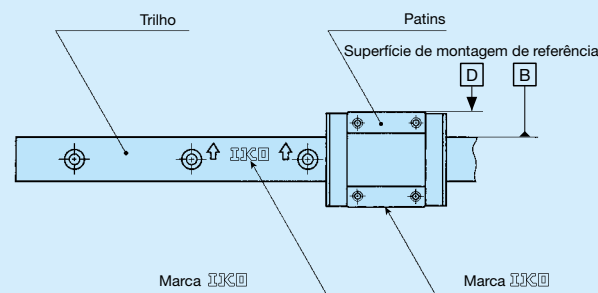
Superfície de montagem de referência das séries de tamanho 2 ou superior
